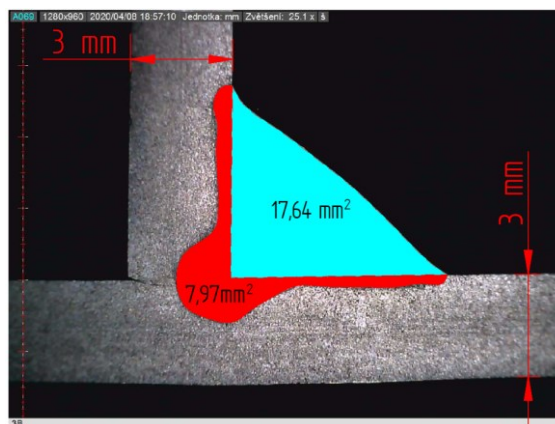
Vzorčky zhotovené metodou TIG [22]
